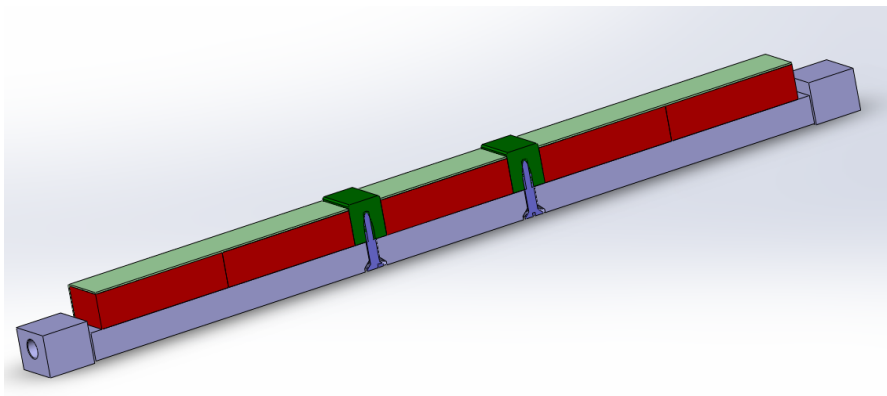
Řez magnetickou lištou s magnety vedle sebe [2]
